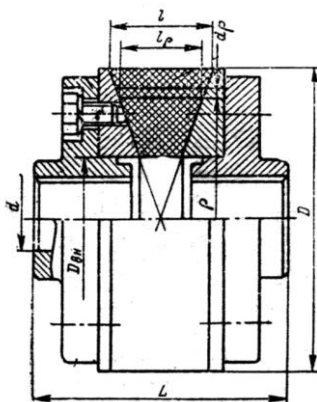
Муфта упругая с резиновой конической шайбой
